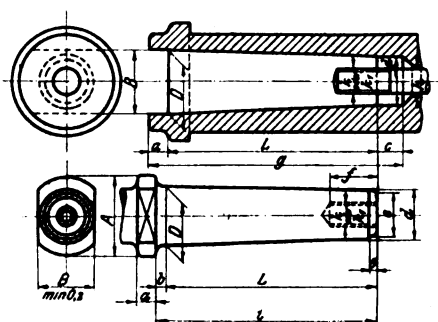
Konusbefestigung für Fräswerkzeuge.
